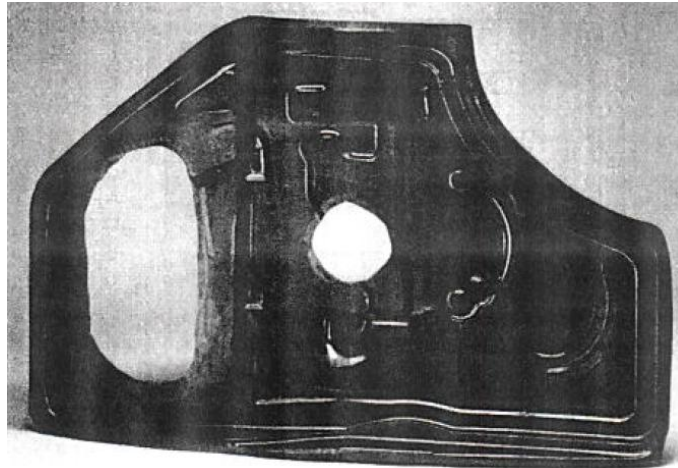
Soldadura láser de blancos a la medida después de ser estampados [2].
